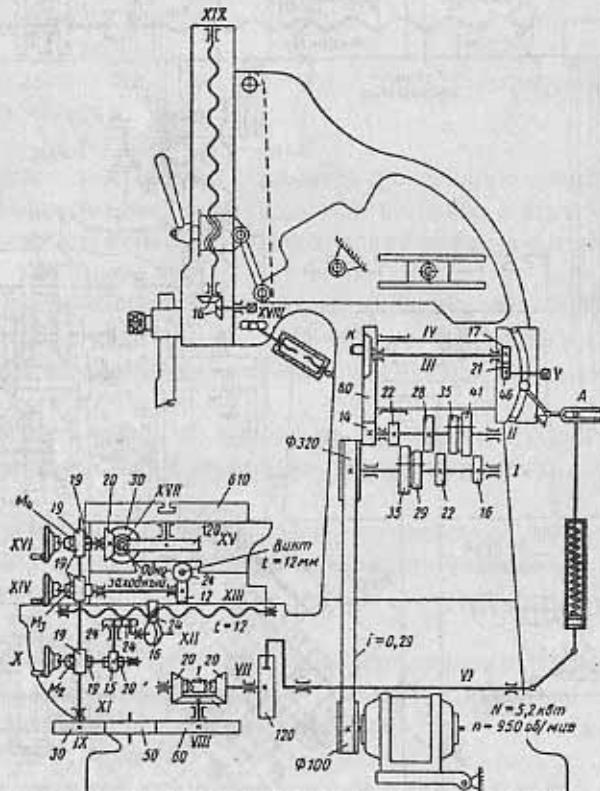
Кинематическая схема долбежного станка мод. 743
